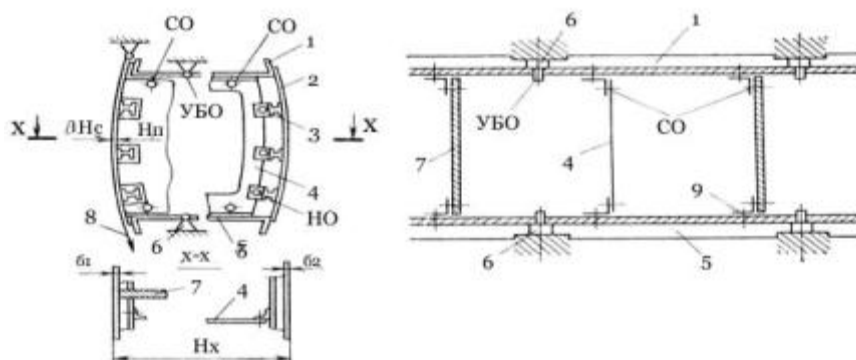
Схема базирования по внутренней поверхности обшивки:
